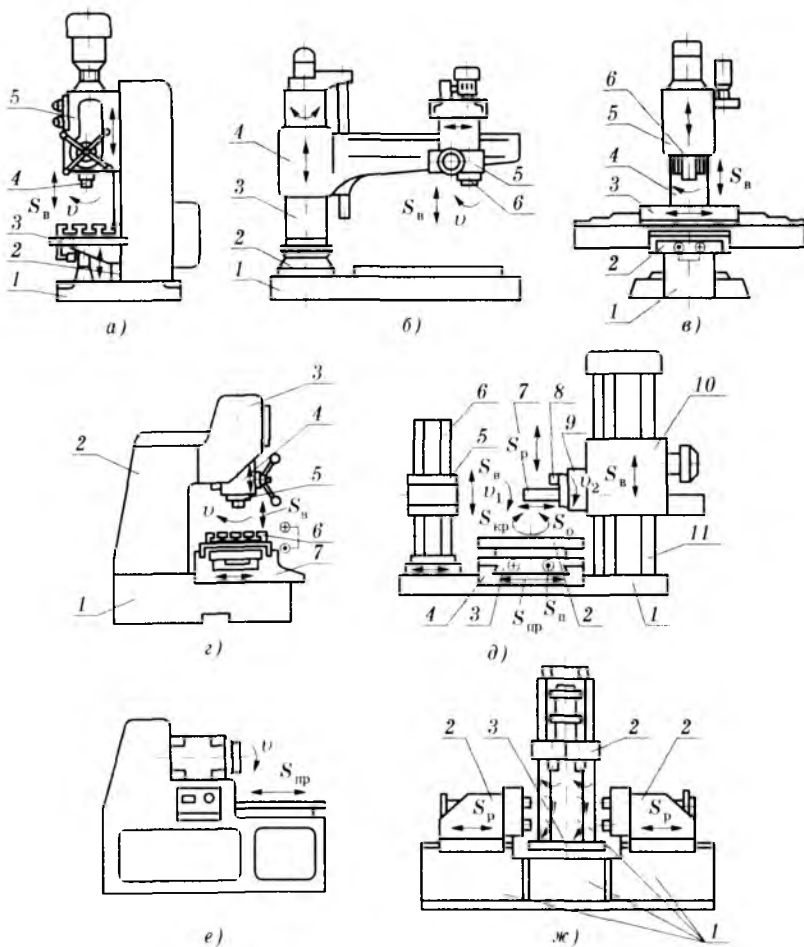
Схемы конструкций сверлильных и расточных станков:
